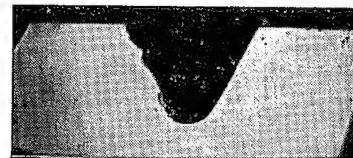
Макроструктура резьбы, накатанной на заготовке из стали ЭИ481.
